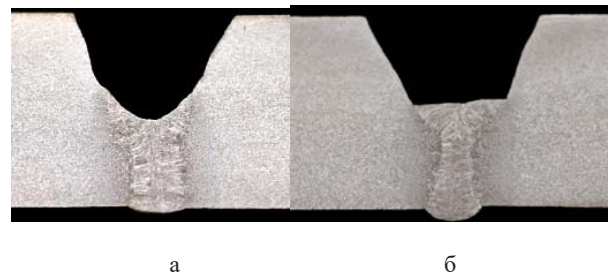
Макрошліфи кореневого шва, виконаного лазерним зварюванням з U-подібною обробкою та притупленням 5 мм а – без присаджувального матеріалу; б – з присаджувальним матеріалом
